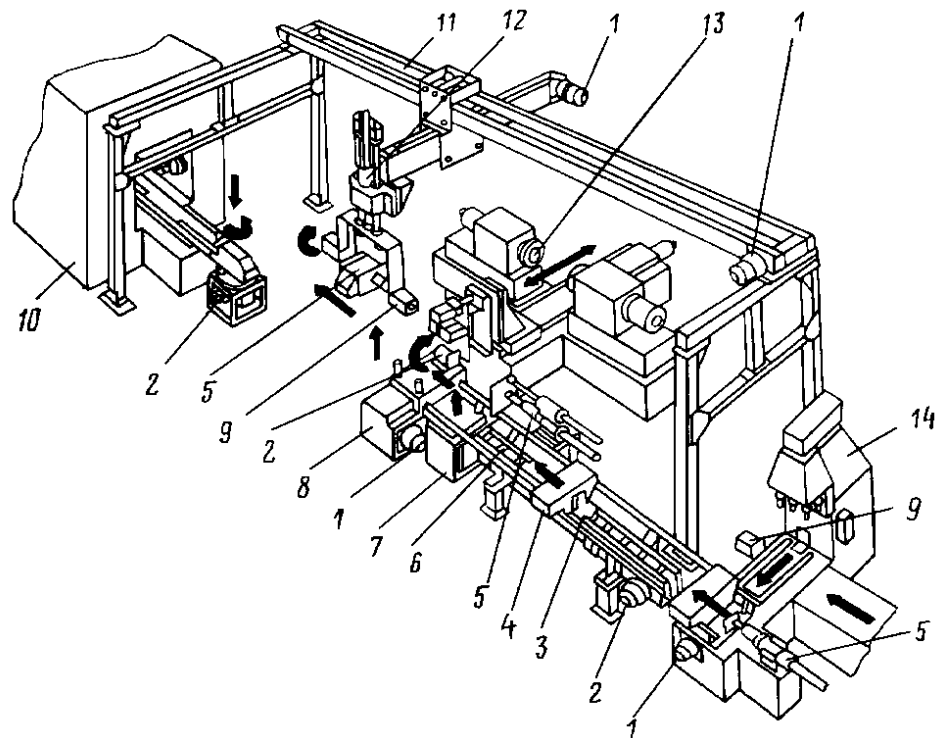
Ділянка автоматичної лінії для оброблення корпусних деталей, оснащена механічними руками і роботом Motohand: 1 – електродвигуни з черв'ячними редукторами; 2 – електродвигуни з зубчастими редукторами; 3 – конвеєр; 4 – заготовка корпусної деталі; 5 – механічна рука для переміщення заготовок уздовж осі конвеєра; 6 – механічна рука; 7 – піднімальний механізм; 8 – завантажувальний стіл; 9 – захоплювач з електроприводом; 10 – тунельна установка для подальшої обробки (миття і т. П.); 11 – рухома траверса (стрілками показані напрямки руху при розвантаженні деталей і передачі їх в тунельну установку 10); 12 – робот Motohand; 13 – поздовжньо-фрезерний верстат; 14 – багатшпindelний вертикально-свердлильний верстат
